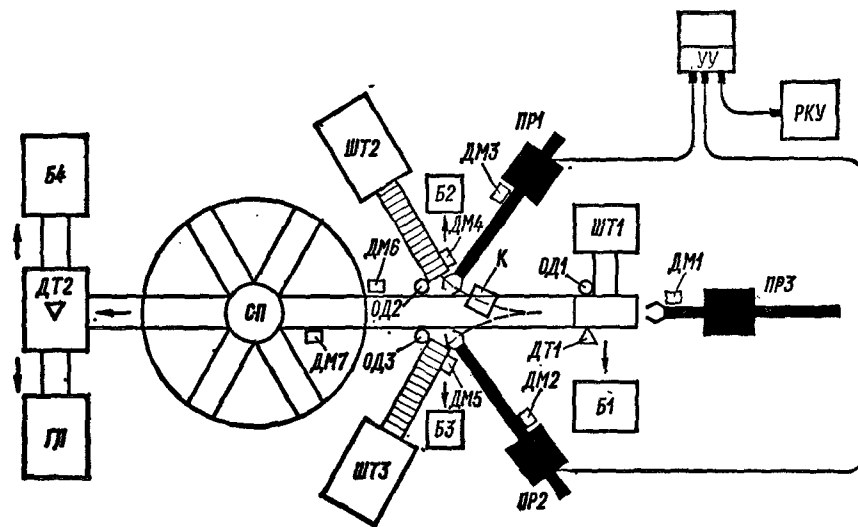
Линия автоматической сборки трансформаторов на базе ПР с адаптивным управлением:
